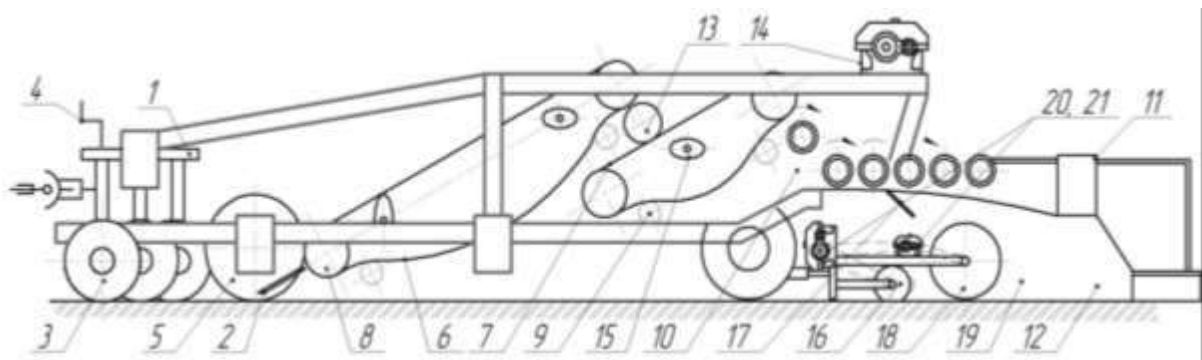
Конструктивно-технологічна схема машини для збирання цибулі-сіянки: 1 – рама; 2 – леміш; 3 – колеса ходові; 4 – механізм регулювання глибини підкопування; 5 – ніж дисковий; 6, 7 – основний і допоміжний сепарувальні елементи; 8, 9 – ботвопротягувальний і підтримувальний ролики; 10 – роликовий сепаратор; 11 – лоток звужувальний; 12 – утворювач валка; 13 – ботвоудаляювач; 14 – редуктор; 15 – струшувачі еліптичні; 16 – рама котка-ложеутворювача; 17 – лоток сходження домішок; 18, 19 – спіральний і циліндричний вальці; 20, 21 – гідромотори приводу вальців котка-ложеутворювача.
